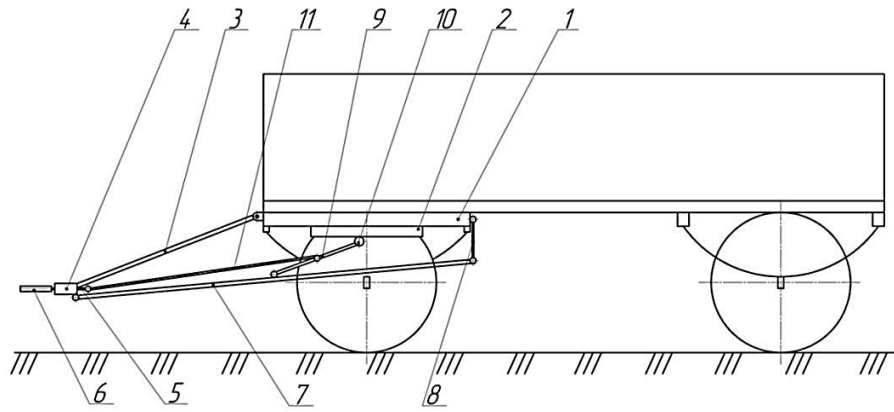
Схема тягово-догрузочного устройства к прицепу: 1 – рама поворотной тележки прицепа; 2 – упор; 3 – дышло; 4 – муфта; 5 – кронштейн; 6 – тяговое кольцо; 7 – балка; 8 – серьга; 9 – маятник; 10 – ролик; 11 – тяга
